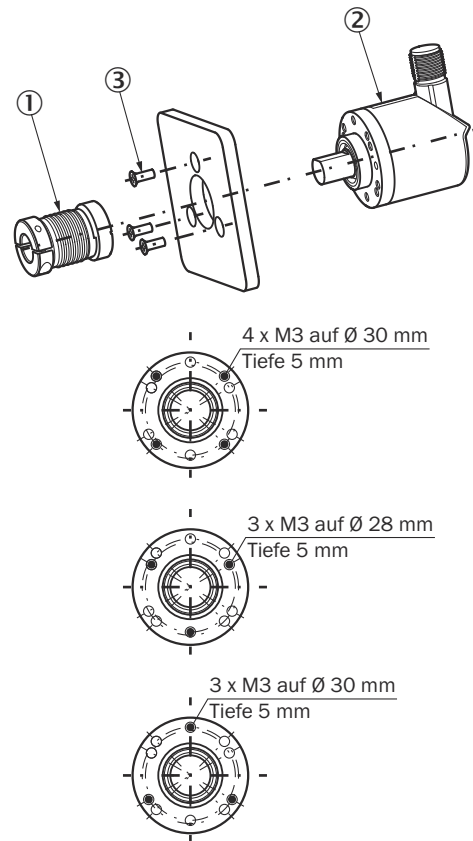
Anbau über flanschseitige Gewindebohrung
